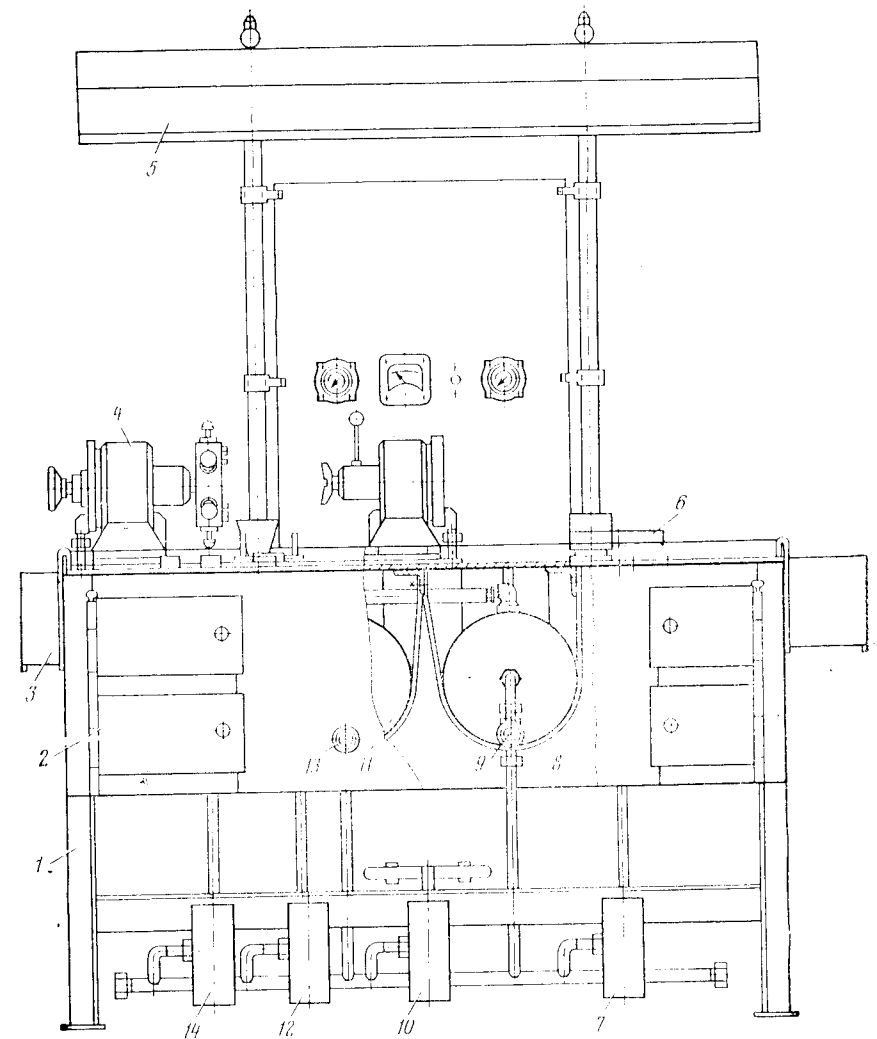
Стенд-верстак для ремонта тормозных приборов
